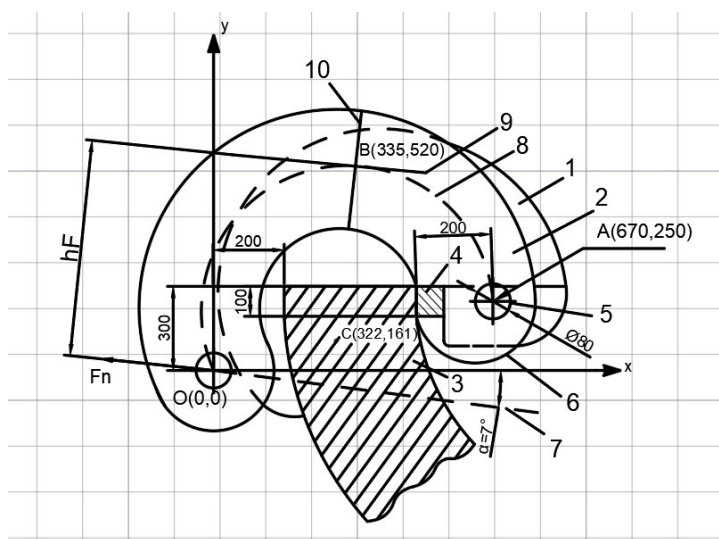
Конструктивная схема захватного устройства: 1 – захват; 2 – рычаг; 3 – эллиптическое днище; 4 – вставка; 5 – ось вращения; 6 – кулачок (контактная поверхность рычага); 7 – силовая линия; 8 – геометрическая ось рычага; 9 – касательная к геометрической оси; 10 – поперечное сечение [Structural diagram of the gripper: 1 – gripper; 2 – lever; 3 – elliptical bottom; 4 – insert; 5 – axis of rotation; 6 – cam (contact surface of the lever); 7 – power line; 8 – geometric axis of the lever; 9 – tangent to the geometric axis; 10 – cross section]
